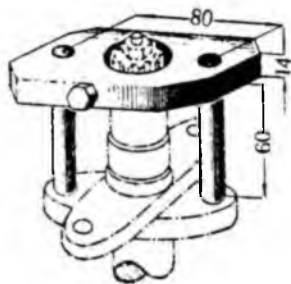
Приспособление для разборки и сборки подкачивающих помп ЧТЗ.
